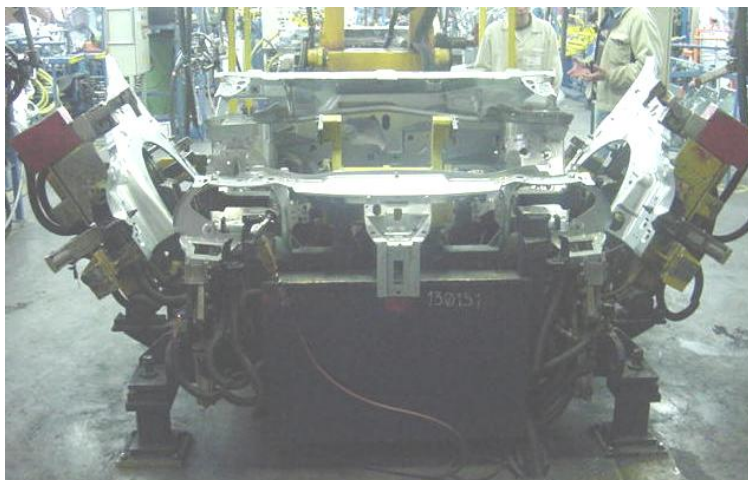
EXEMPLO DE CHAPAS DE AÇO SOLDADAS
